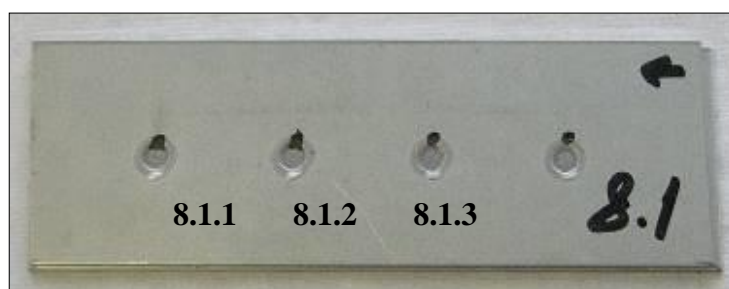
Внешний вид точечной контактной сварки образца № 8.1
